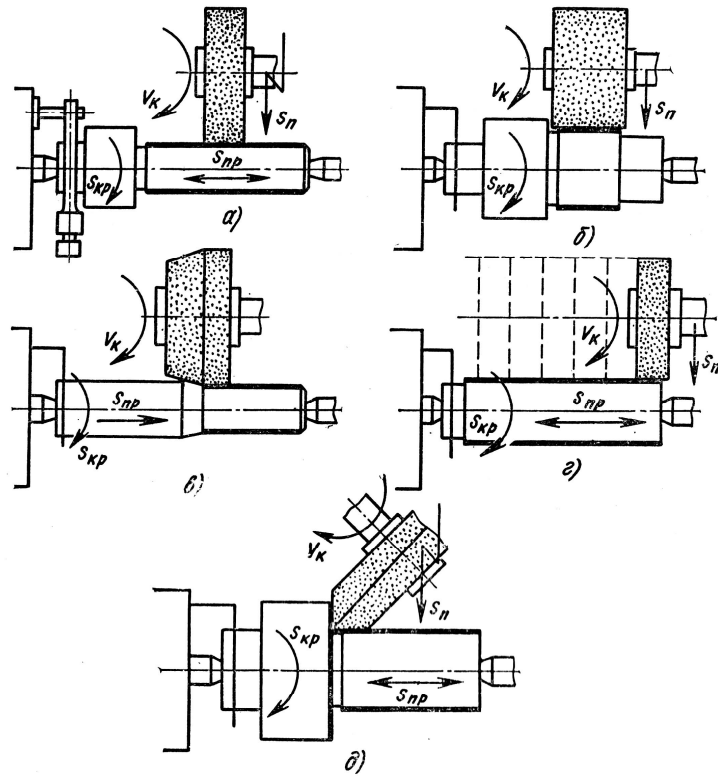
Схеми обробки заготовок на круглошліфувальних верстатах
